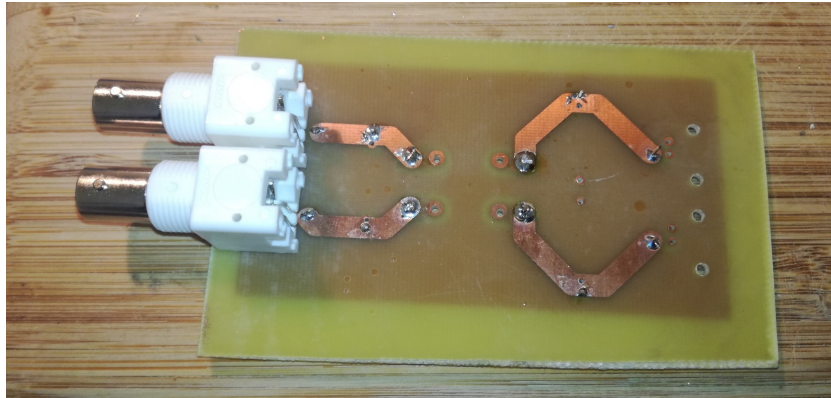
Placa en proceso de montaje. Taladrado y soldado de componentes.
